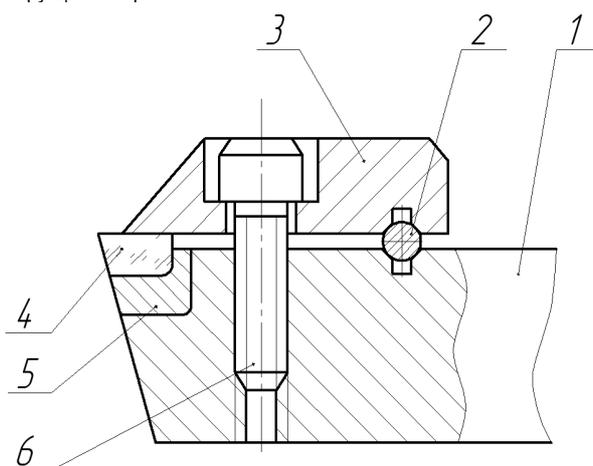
Резец с механическим креплением искусственного алмаза с использованием специальной подушки: 1 – державка резца; 2 – штифт; 3 – накладка; 4 – алмаз; 5 – подушка; 6 – винт
